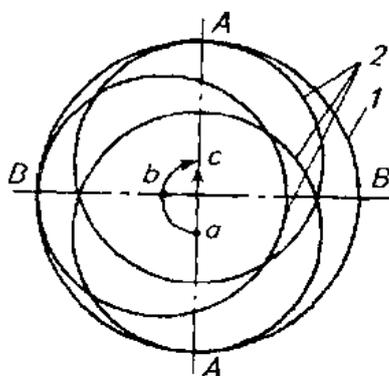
Схема движения кольца в поршневой канавке:
